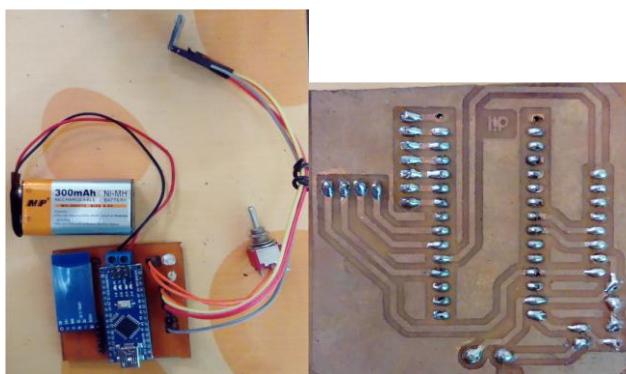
Placa del sistema móvil y pistas soldadas
